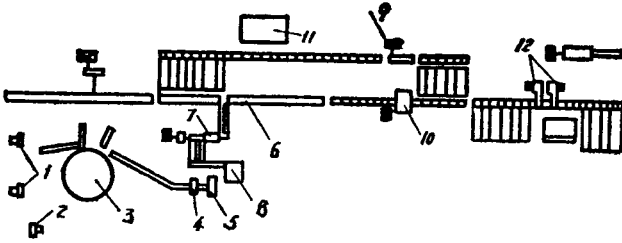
生产不锈钢钢管的顶管机组平面布置图
